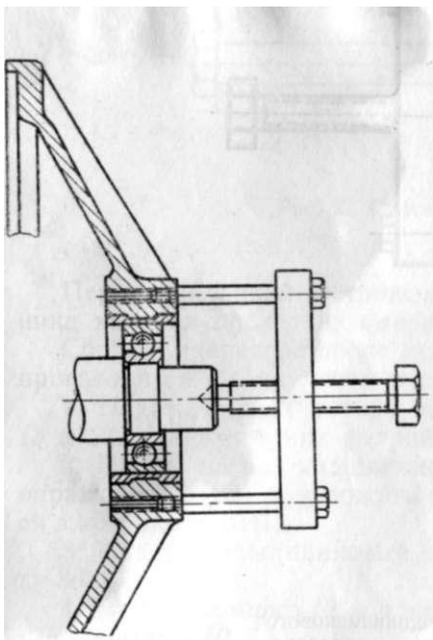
Снятие подшипникового щита со стороны контактных колец
